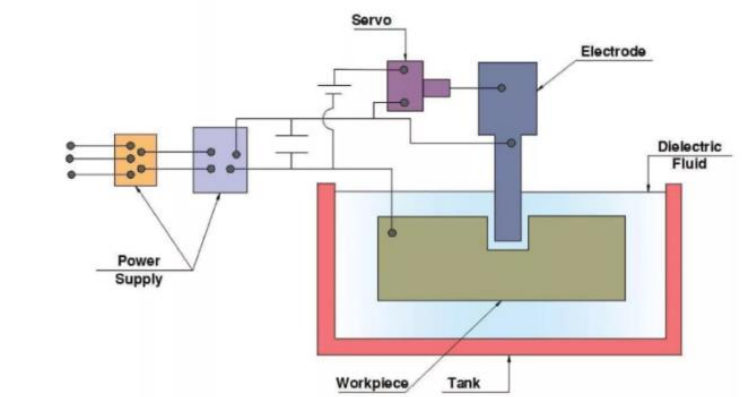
Принцип работы электроэрозионного копировально-прошивочного станка
